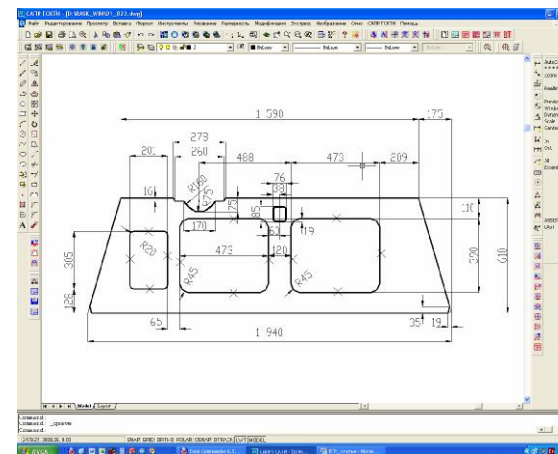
Чертеж детали „Лист носовой верхний” корпуса БТР-3Е
